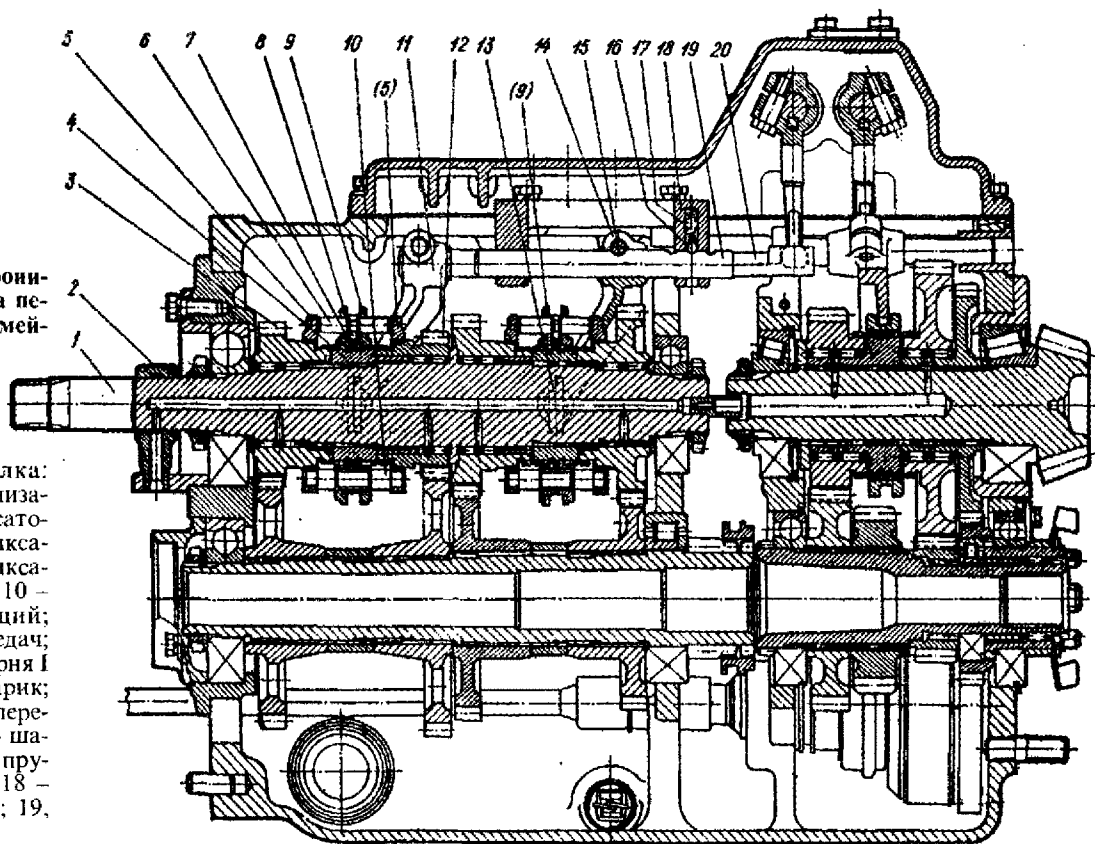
Синхронизирующая коробка передач тракторов семейства МТЗ: 1 – первичный вал; 2 – маслоподводящая муфта; 3 – ведущая шестерня II передачи; 4 – втулка; 5 – кольцо синхронизатора; 6 – палец фиксатора; 7 – пружина фиксатора; 8 – шарик фиксатора; 9 – каретка; 10 – палец блокирующий; 11 – вилка I и II передач; 12 – ведущая шестерня I передачи; 13 – сухарик; 14 – вилка III и IV передач; 15 – болт; 16 – шарик фиксатора; 17 – пружина фиксатора; 18 – корпус фиксатора; 19, 20 – поводок
